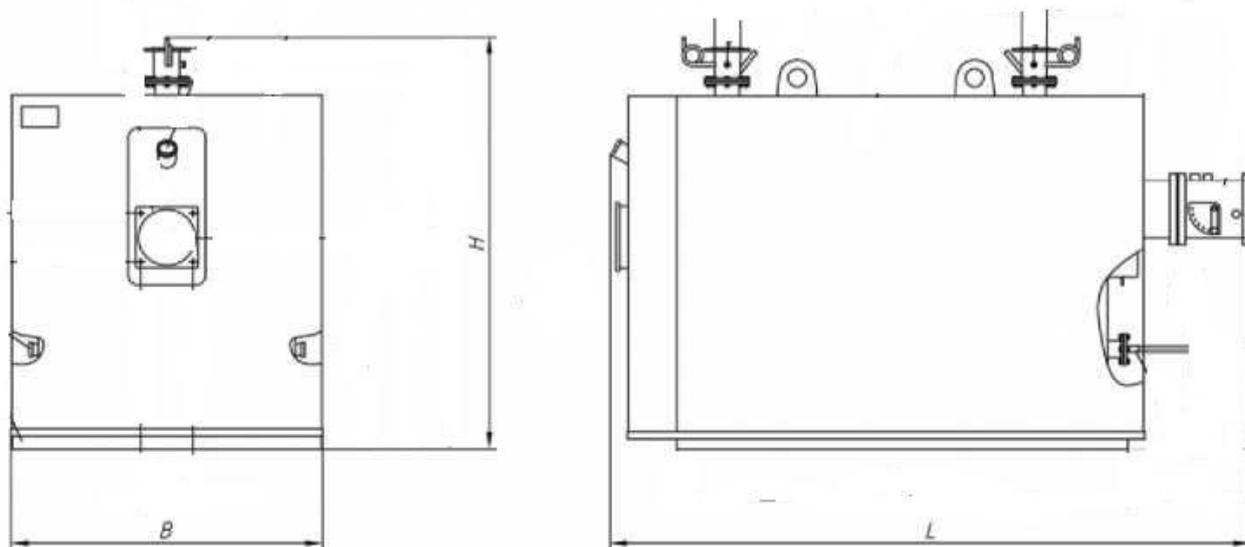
Устройство и габариты компоновки котла КВСА
